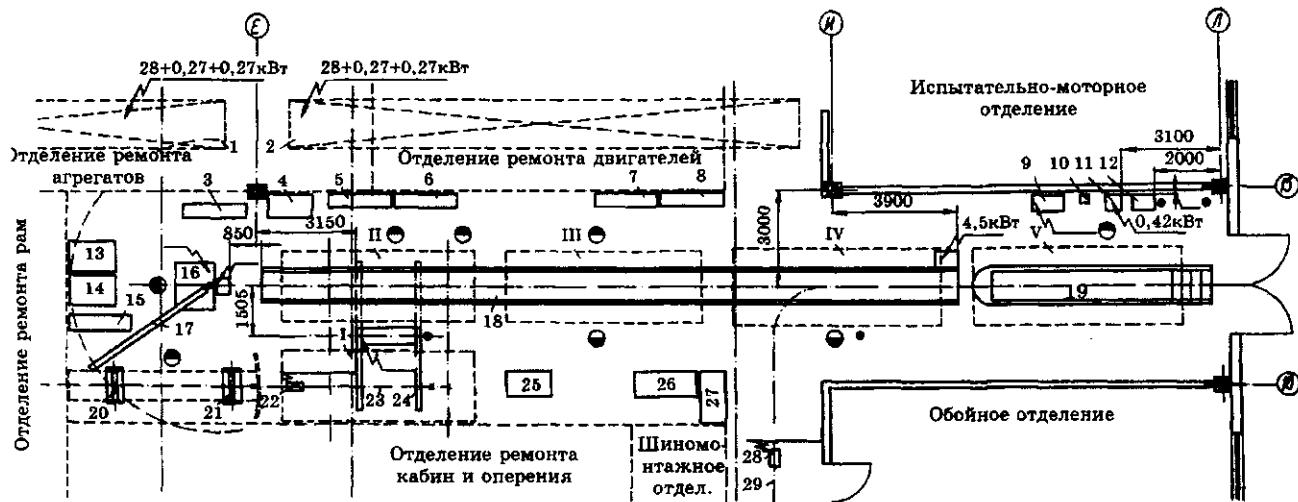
Планировка участка общей сборки грузовых автомобилей: I — пост сборки мостов с рамой; II — IV — посты сборки автомобиля на поточной линии; V — пост регулировки и заправки автомобиля эксплуатационными материалами; 1, 2 — кранбалки (подвесные); 3, 6, 8, 15 — стеллажи полочные; 4, 25 — верстаки слесарные; 5, 7 — стеллажи секционные; 9 — солидолонагнетатель; 10 — бак для заправки тормозной жидкостью; 11 — бензоколонка; 12 — установка для централизованной смазки и заправки автомобилей; 13, 14 — контейнеры для рессор; 16 — стенд для сборки мостов с рессорами; 17 — консольный поворотный кран; 18 — конвейер грузонесущий; 19 — канава узкая; 20, 21 — подставки под раму; 22, 28 — тали электрические; 23, 29 — монорельсы; 24 — кантователь; 26 — стеллаж для радиаторов и баков топливных; 27 — стеллаж для колес
